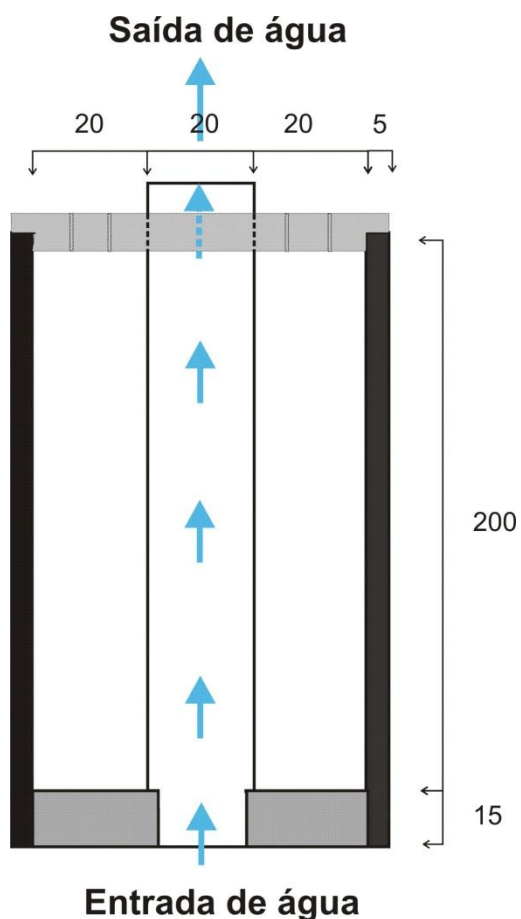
Dimensões do conjunto lingoteira/ sistema de refrigeração.
